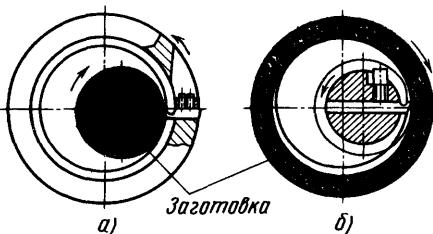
Схема нарезания резьбы вихревым методом:
